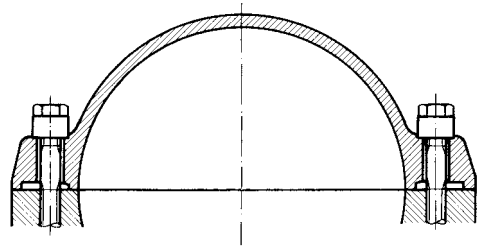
Assemblage d'une bâche de turbomachine.
